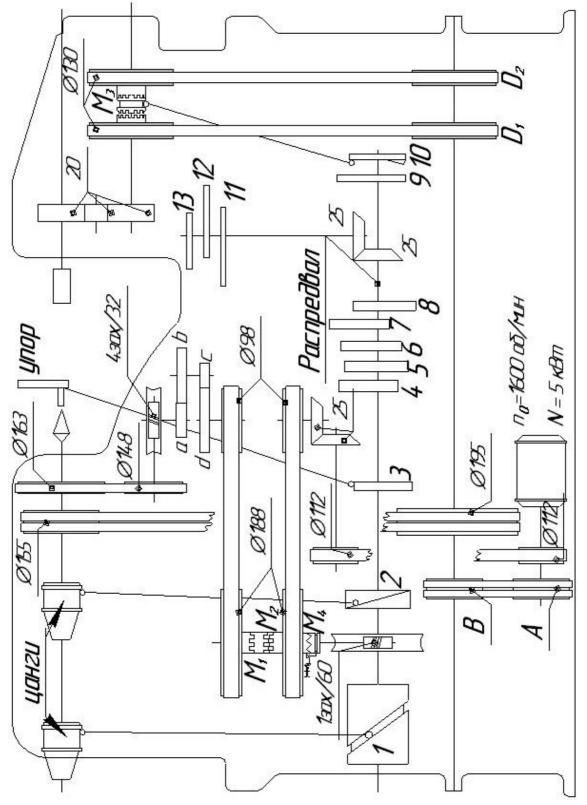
Кинематическая схема одношпиндельного токарно-револьверного автомата
